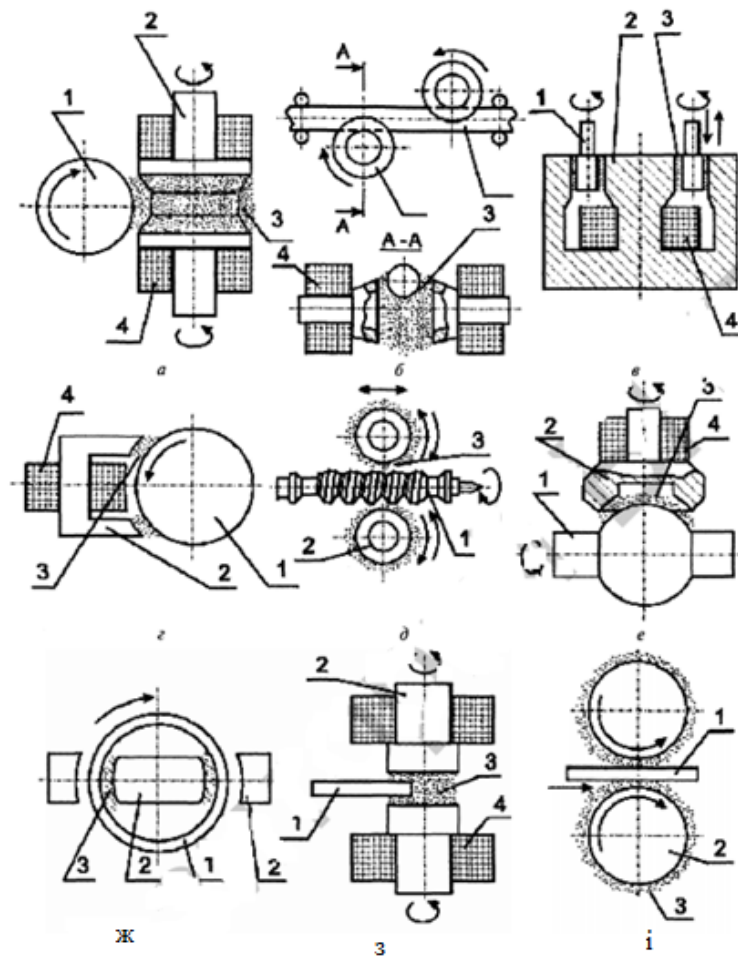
Схеми МАО: а) валів; б) прутків та труб; в) поверхонь тіл обертання; г) багатогабаритних валів; д) винтів; е) сфер; ж) отворів; з) кромки; і) листів та стрішок; 1)оброблювана заготовка; 2)полюсний нанакінецьник; 3)фероабразивний порошок; 4) електроагнітні катушки
